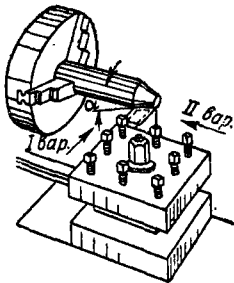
Схема обтачивания конической поверхности широким резцом.
